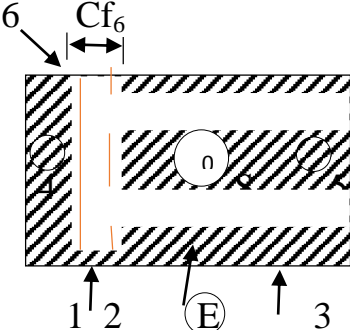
Cassette coté mal (Vue de coupe sur plan de surface)
